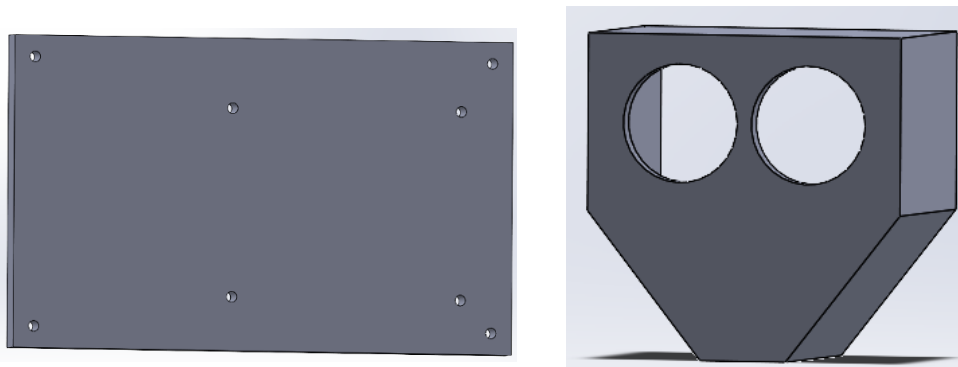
Piezas finales: a) tapa apertura frontal, b) cabeza
